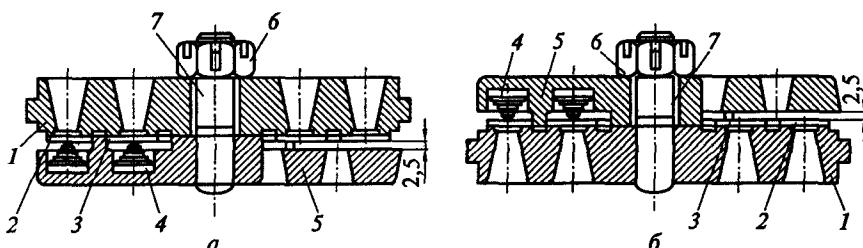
Всасывающий (а) и нагнетательный (б) клапаны компрессора КТ-6:
